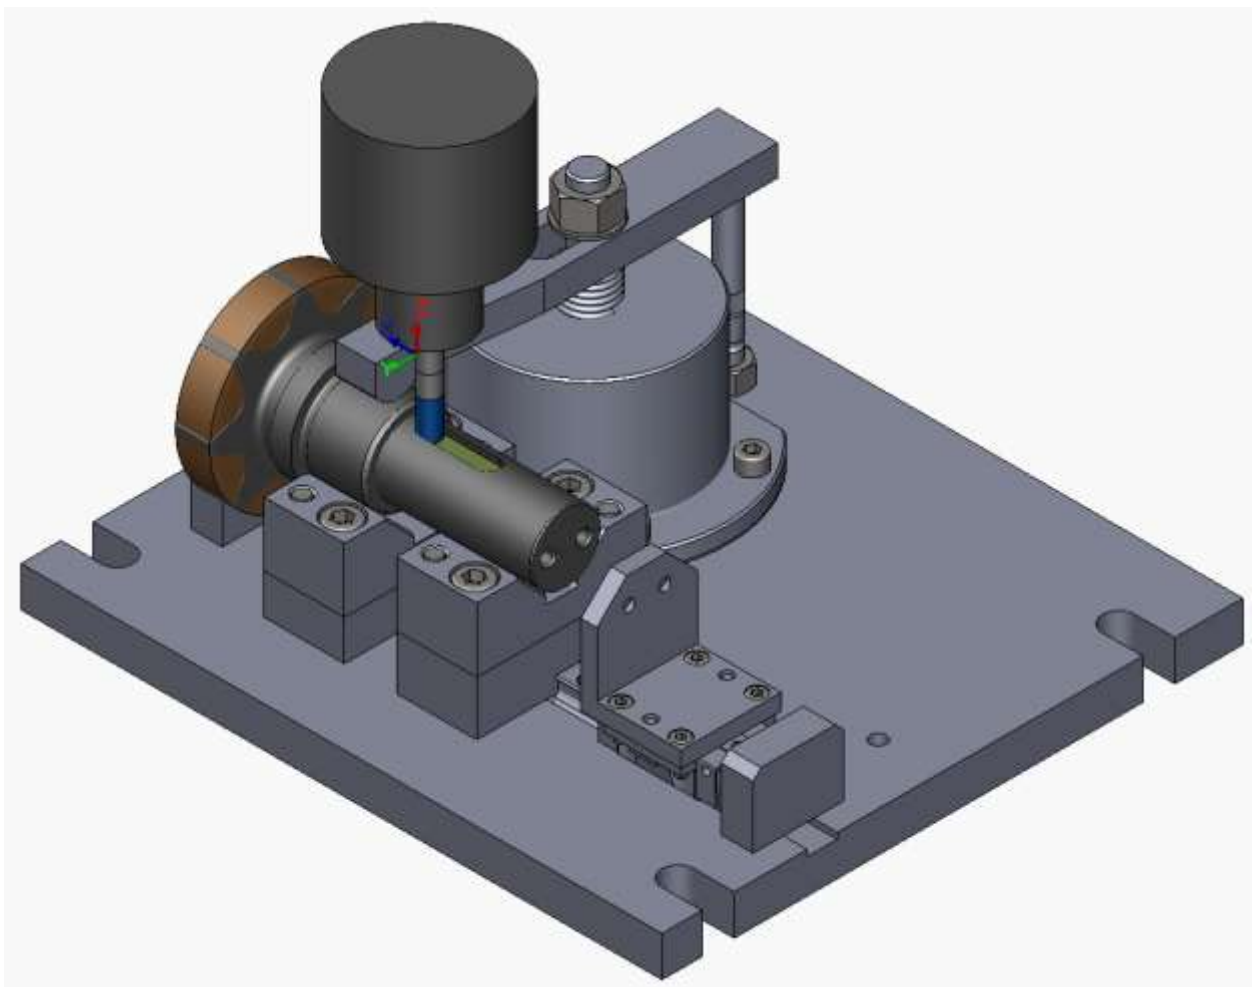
Імітація обробки на фрезерну операцію 040 Установ 1
